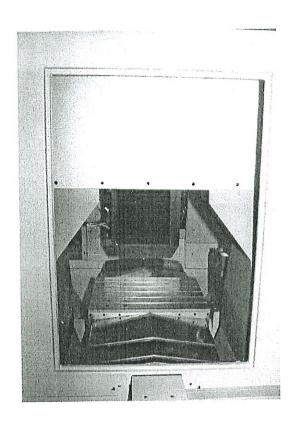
Rüstzugang nur zur Reinigung Zum Reinigen Blech auf Maschinenrückseite abnehmen durch lösen der Schrauben mit Werkzeug.
